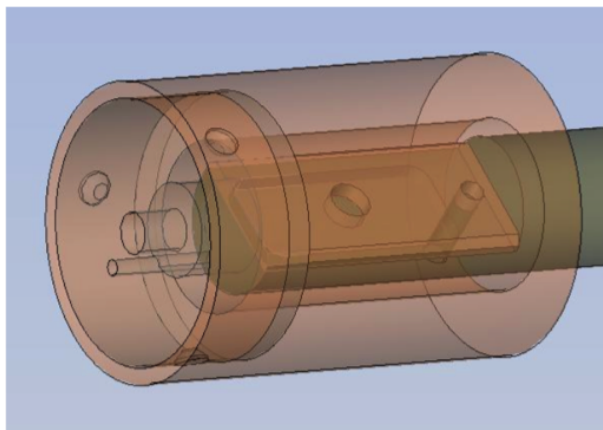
Struttura del portacampione: dettaglio dove si nota la lavorazione del cilindro di pirofillite.
